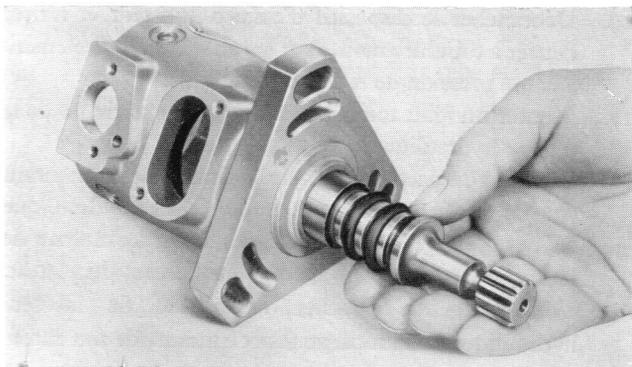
Démontage de l'arbre d'entraînement cannelé
